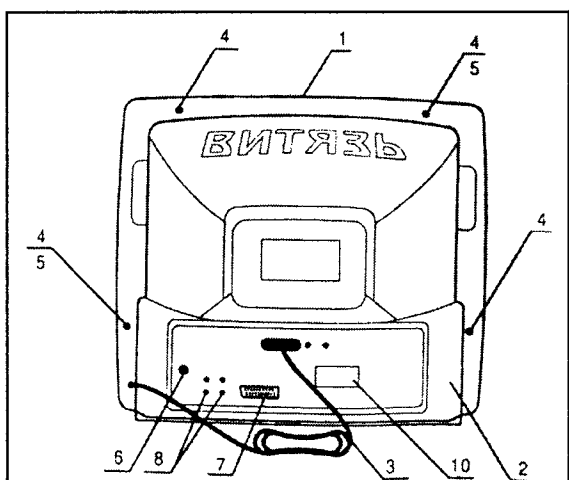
Вид телевизора "Витязь" в корпусе OMEGA со стороны кожуха: 1 — корпус; 2 — кожух; 3 — сетевой шнур; 4 — винты крепления кожуха; 5 — место пломбировки; 6 — розетка для подключения антенны MB, ДМВ; 7 — разъем EXTERNAL для подключения внешних устройств через соединитель типа SCART; 8 — соединители: AUDIO IN (вход звука); AUDIO OUT (выход звука); VIDEO IN (вход видео); VIDEO OUT (выход видео); 10 — заводской номер
